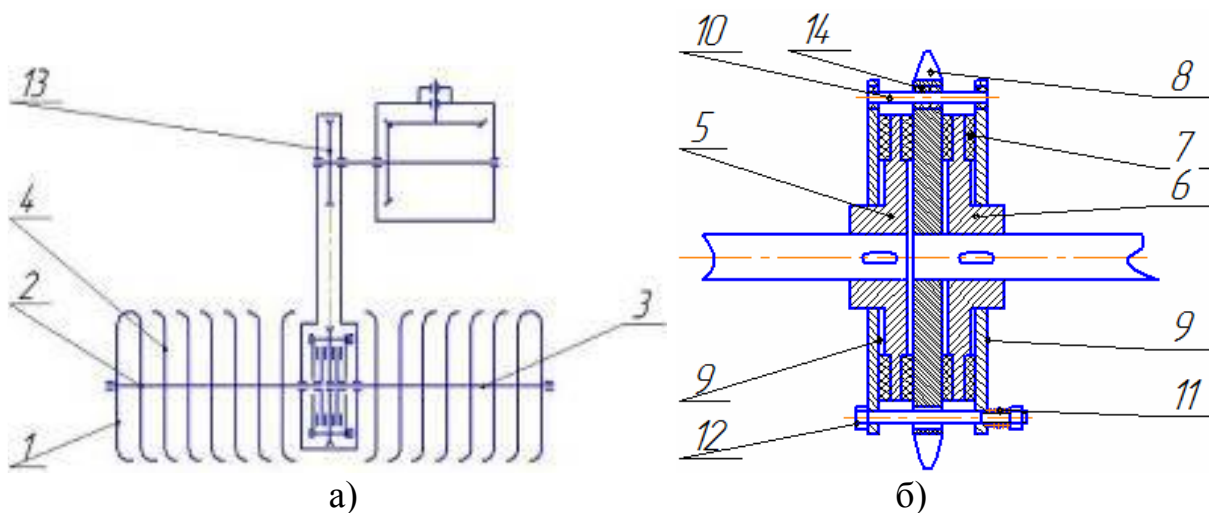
Конструктивно-технологическая схема лесной фрезерной машины с двухпоточным предохранительным устройством с центральным приводом (вид а) и двухпоточный предохранитель (вид б):
